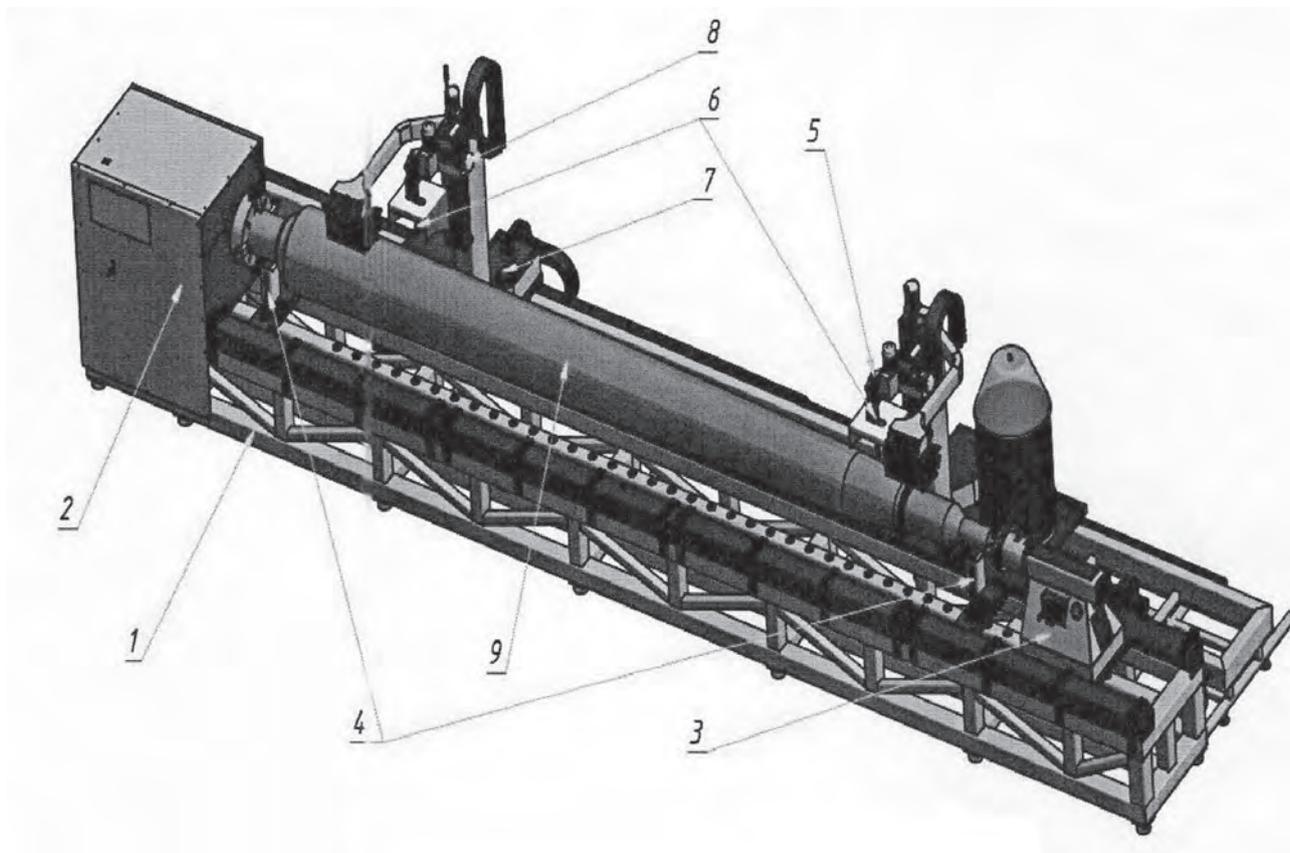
Внешний вид установки для наплавки: 1 – каркас; 2 – передняя бабка; 3 – задняя бабка; 4 – ловители; 5 – механизм подачи проволоки; 6 – горелка; 7 – привод горизонтального перемещения; 8 – привод вертикального перемещения; 9 – наплавляемая деталь
